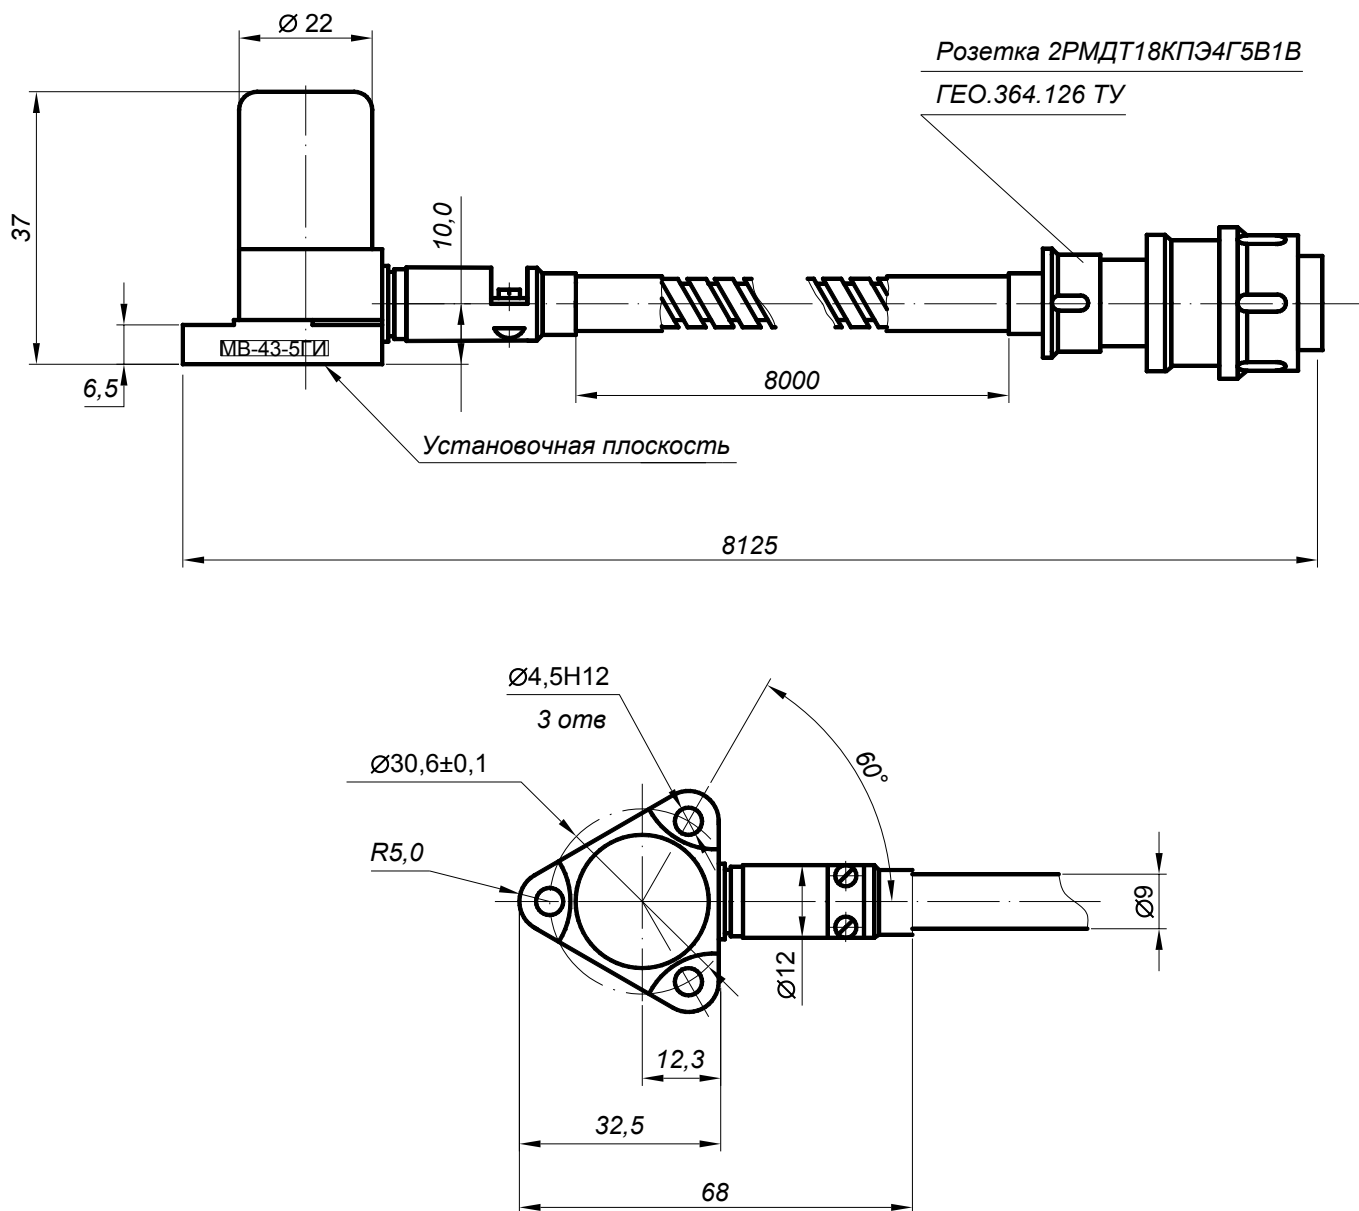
Габаритно-установочные размеры вибропреобразователя МВ-43-5ГИ/8,0
